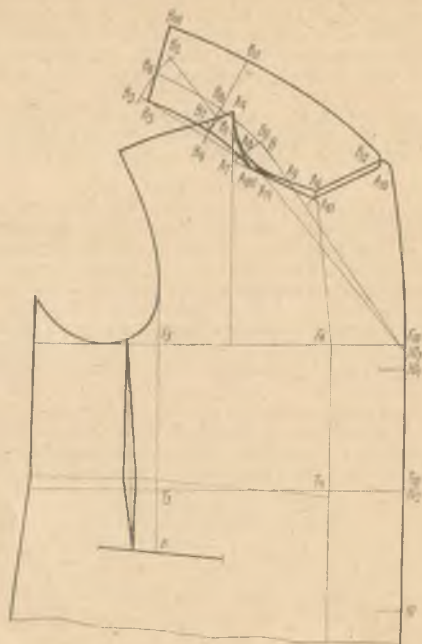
Чертежи выкройки и закрытого воротника для двубортного пальто
